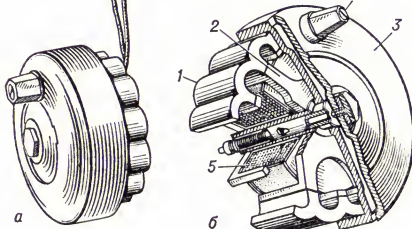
Индуктор с неподвижной обмоткой: а — общий вид; б — разрез: 1 — многополюсный вращающийся постоянный магнит (ротор); 2 — статор из мягкой стали; 3 — вращающийся диск; 4 — рукоятка; 5 — обмотка статора.
